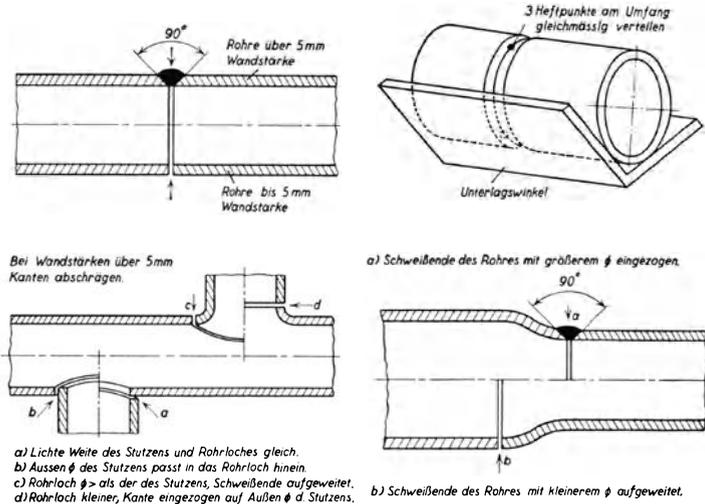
Rohrverbindungen durch Schweißen.
